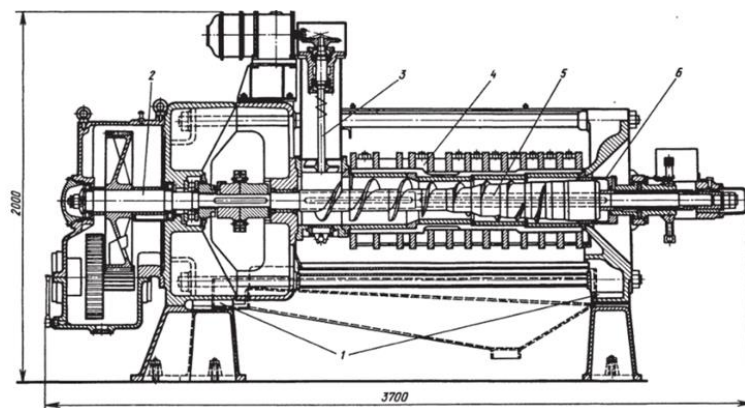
Схема форпреса: ФП 1 – станина; 2 -
